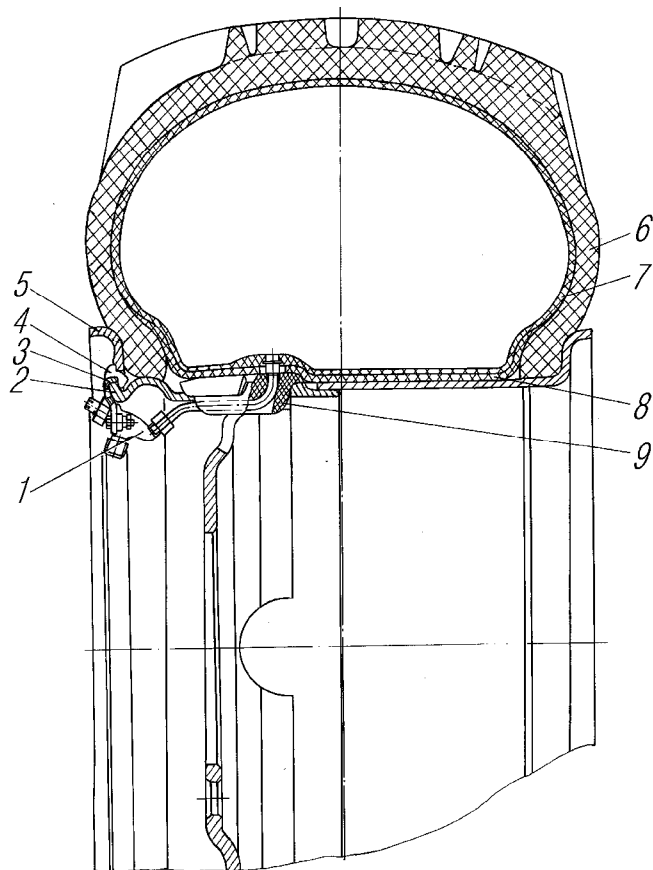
Колесо с шиной в сборе: 1- кран колесный; 2- основание обода с диском; 3- ограничитель замочного кольца; 4- кольцо замочное; 5- кольцо бортовое; 6- покрышка; 7- камера; 8- лента ободная; 9- уплотнитель вентильного паза
